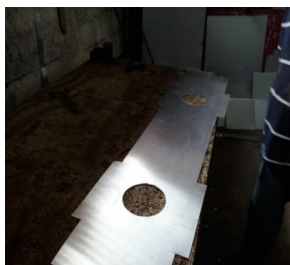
Chapa de Alumínio- Parte externa do Desidratador
